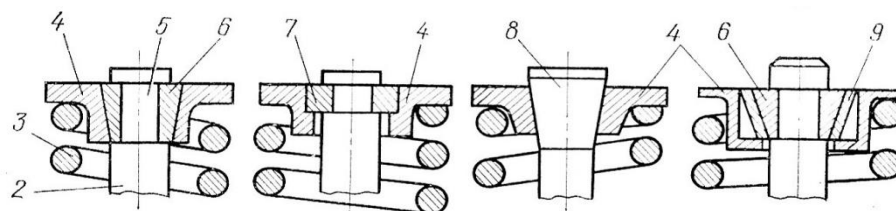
Способы крепления клапанных пружин: 2 – стержень клапана; 3 – пружина; 4 – тарелка; 5 – проточка; 6 – конические сухарики; 7 – цилиндрические сухарики; 8 – конус; 9 – промежуточная втулка
